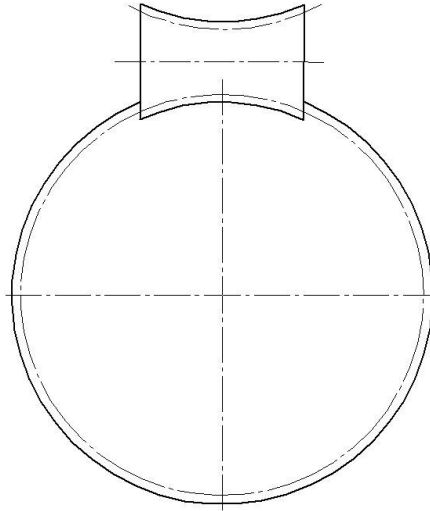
Зацепление гиперboloидного колеса с цилиндрическим косозубым зубчатым колесом
